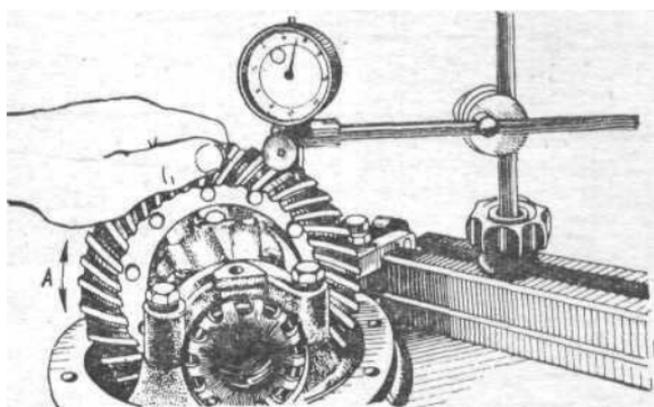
Проверка бокового зазора в зацеплении зубьев шестерен главной передачи индикатором
